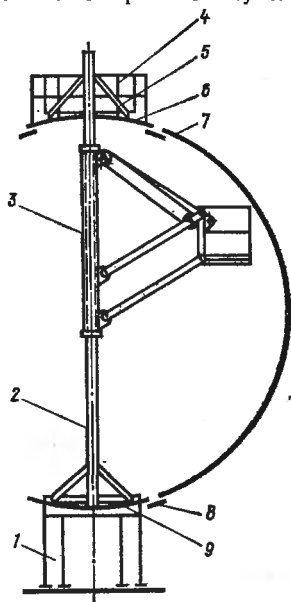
Схема сборки полусферы из штампованных лепестков:
